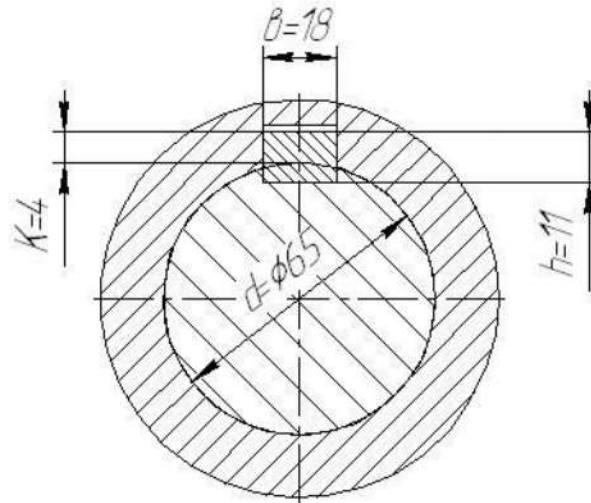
Розрахункова схема шпонкового з'єднання
